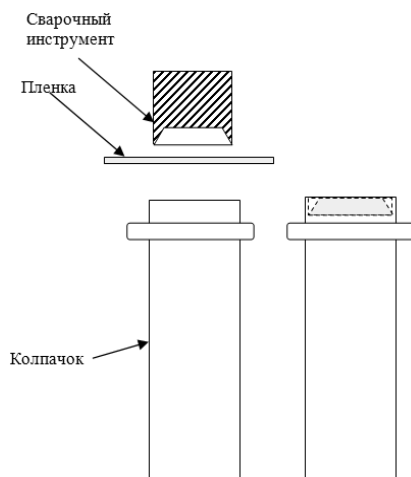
Схема сварки для сварочного инструмента с режущей кромкой диаметром 7,1 мм (СИ2)
